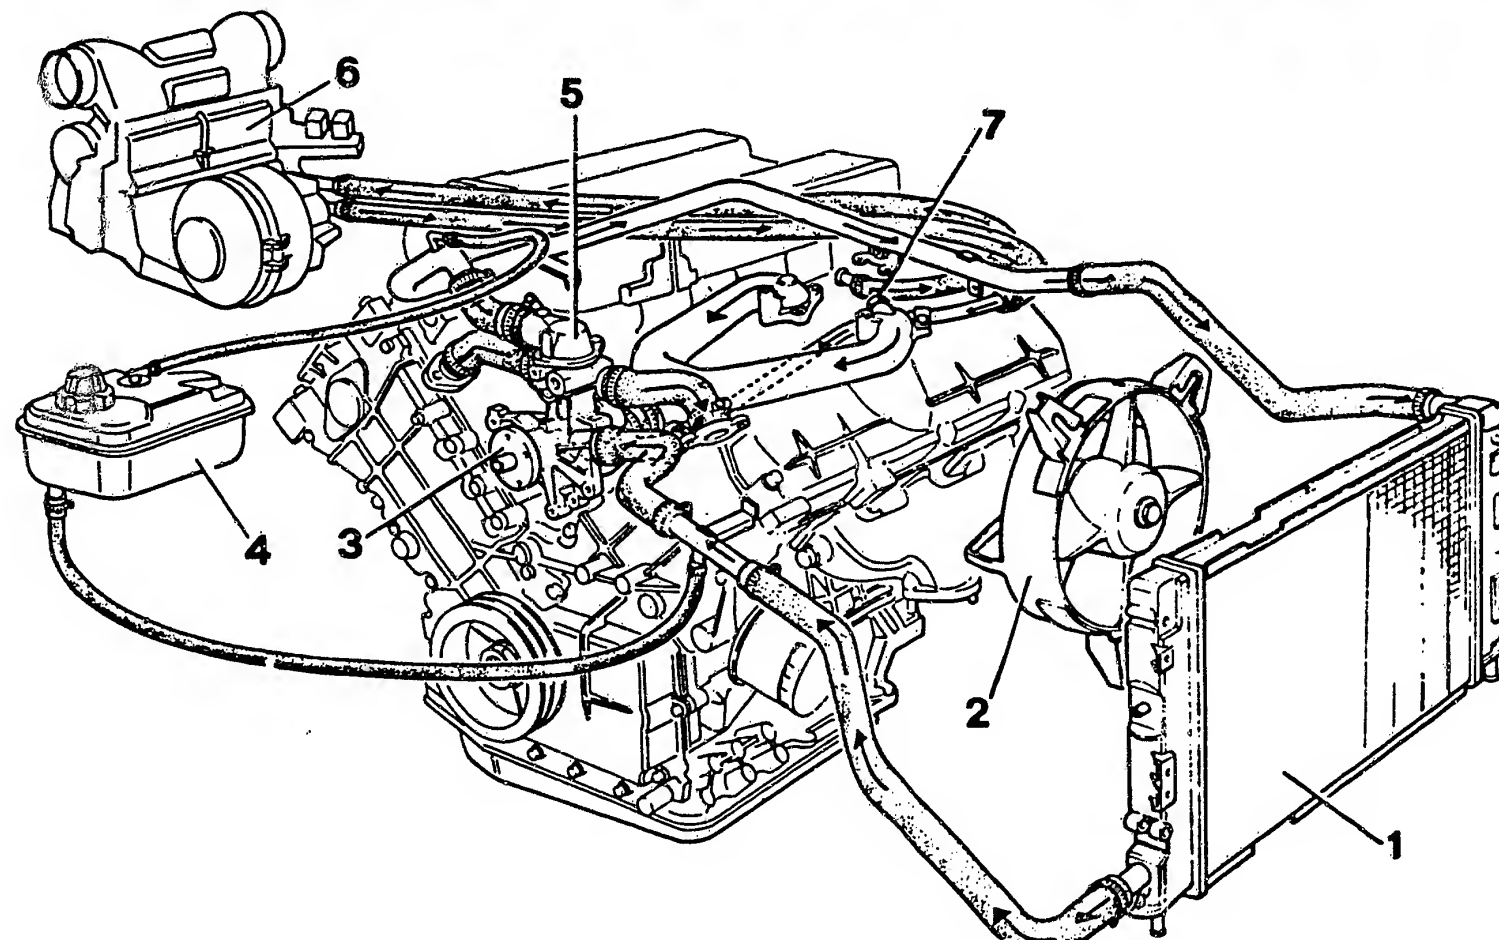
2850 V6-Motor: Kühlkreislauf mit 1 Kühler – 2 Ventilator – 3 Wasserpumpe – 4 Ausgleichsbehälter – 5 Thermostatengehäuse – 6 Heizgebläse – 7 Entlüftungsschraube.
